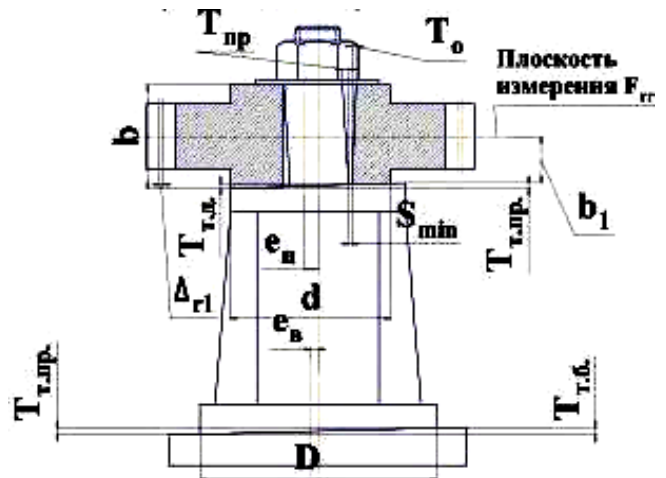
Анализ установки обрабатываемой заготовки на зубофрезерной технологической операции
